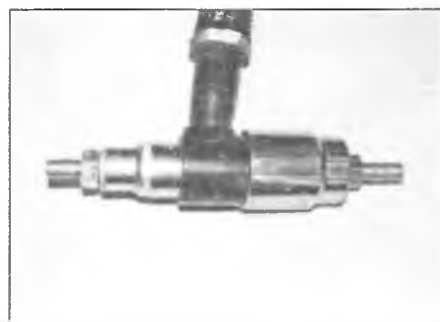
Втулки можно выпрессовывать с помощью торцевых головок или куска трубы подходящего диаметра
